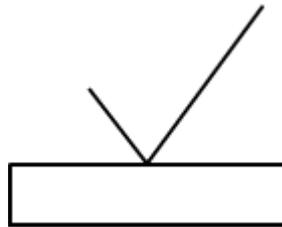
Знак, коли вид механічної обробки не встановлено
